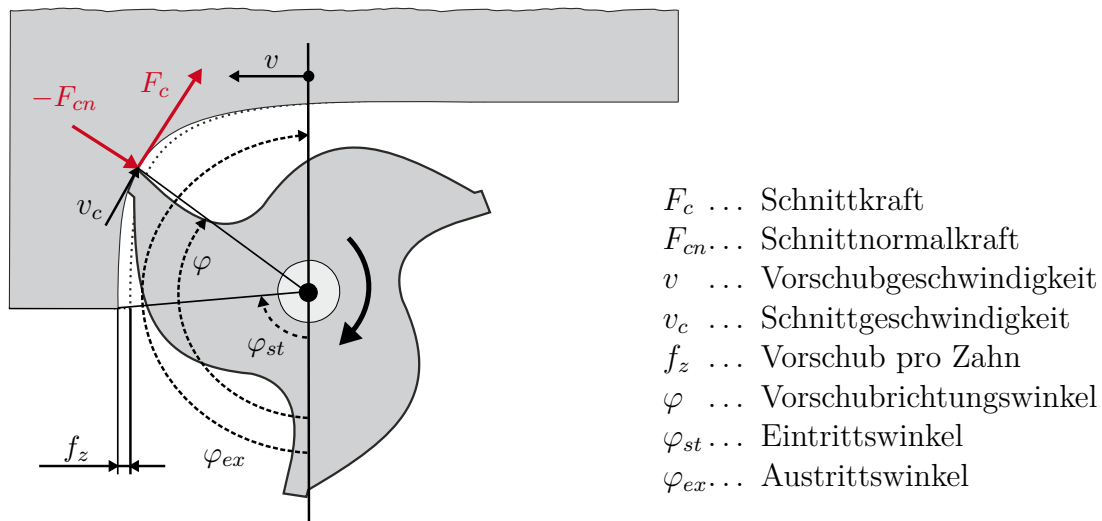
Komponenten der Zerspankraft für ein Scheibenelement des Fräasers gemäß [4].
